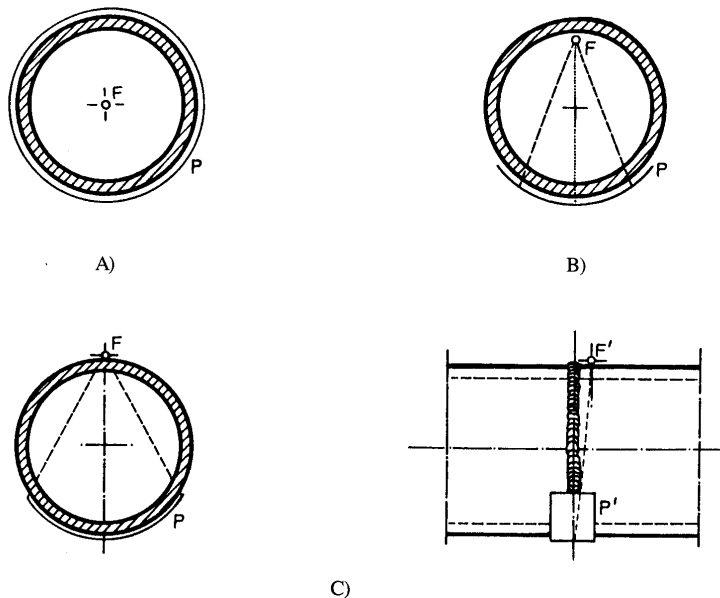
Técnicas usuales para la radiografía de soldaduras circulares en tubos.
